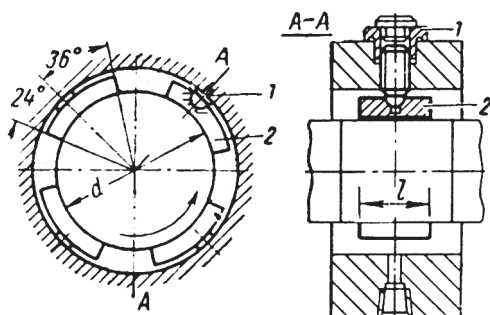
Подшипники скольжения, самоустанавливающиеся по наружной цилиндрической поверхности
